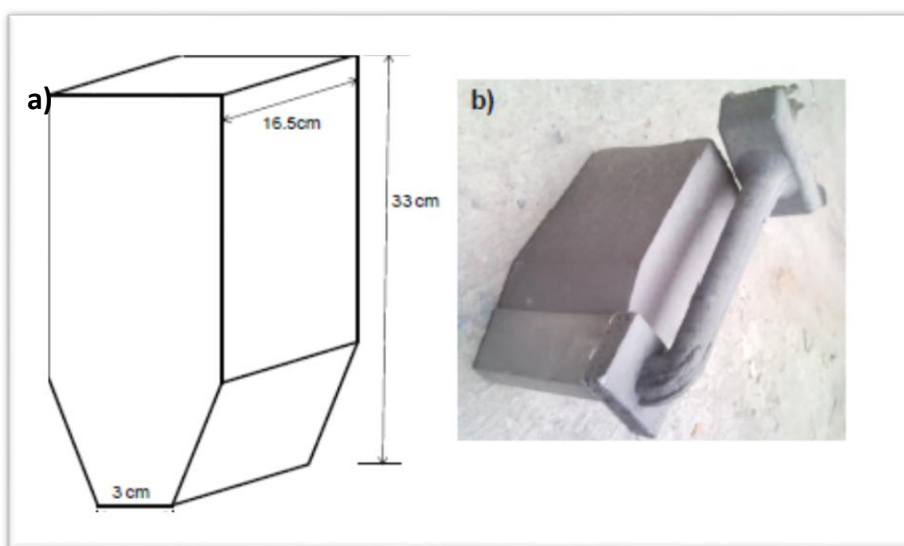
Dimensiones de molde utilizado para el vaciado de muestras, a) imagen dimensiones, b) imagen real.
